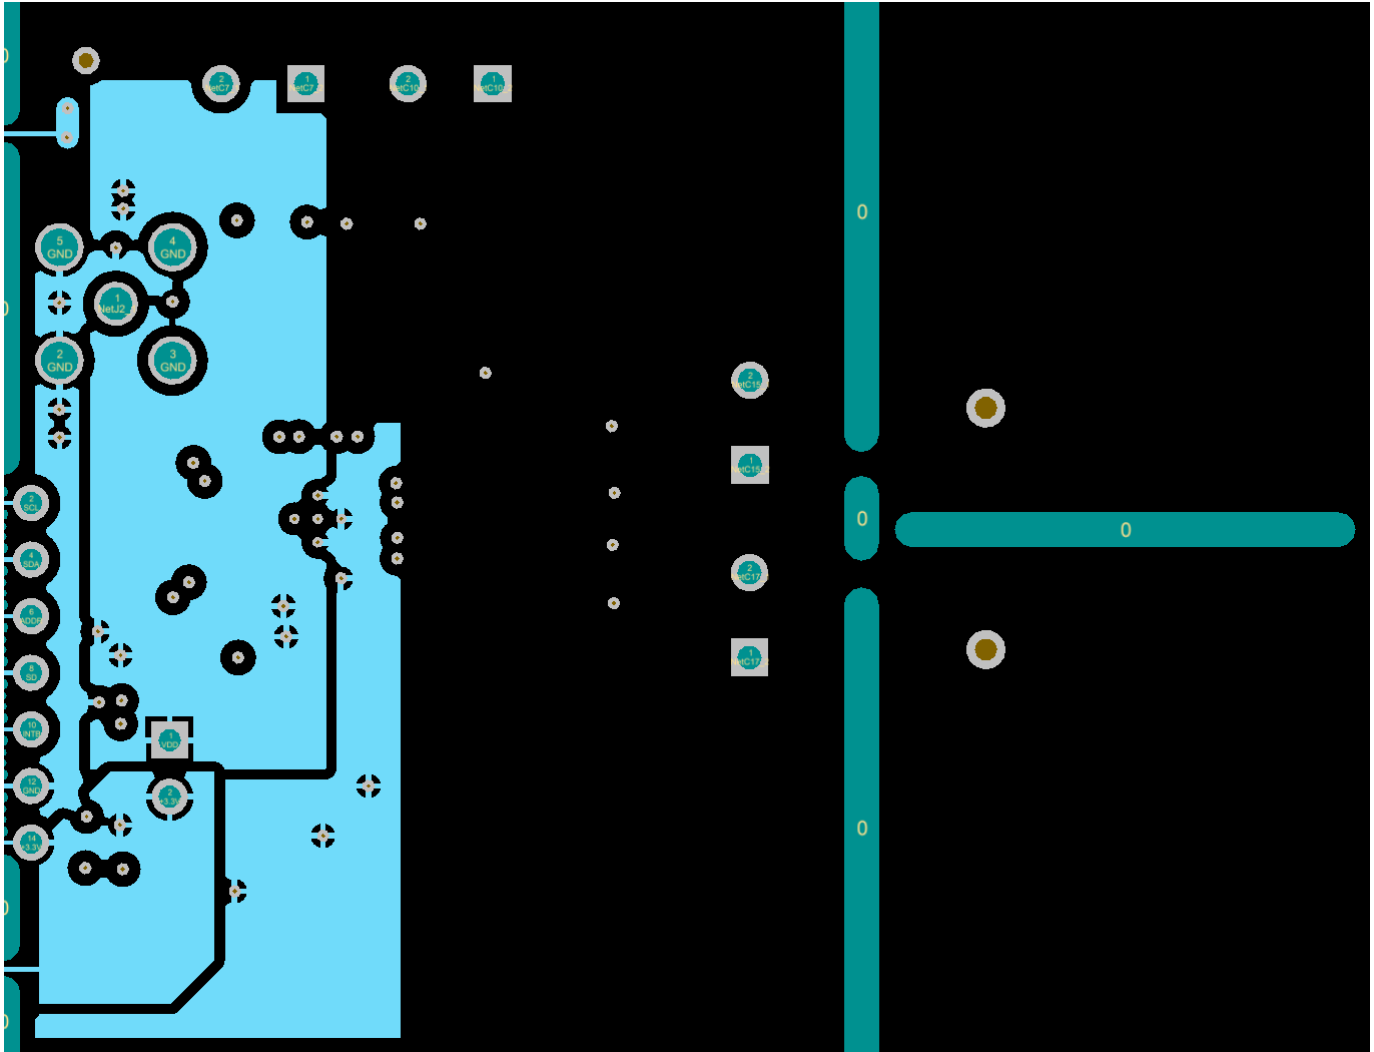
PCB レイアウトの例 : 中間層 2 (電源)
